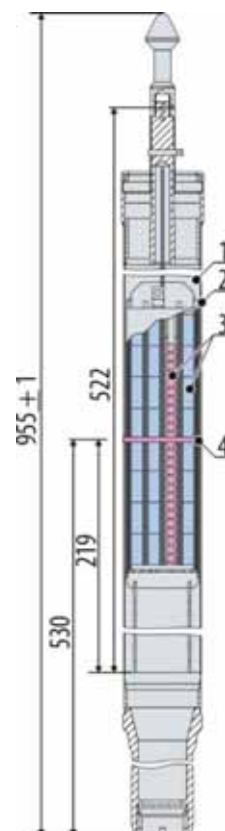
Общий вид облучательного устройства серии «Прометей»: 1 — наружный корпус; 2 — кассета; 3 — образцы; 4 — центральная плоскость активной зоны
